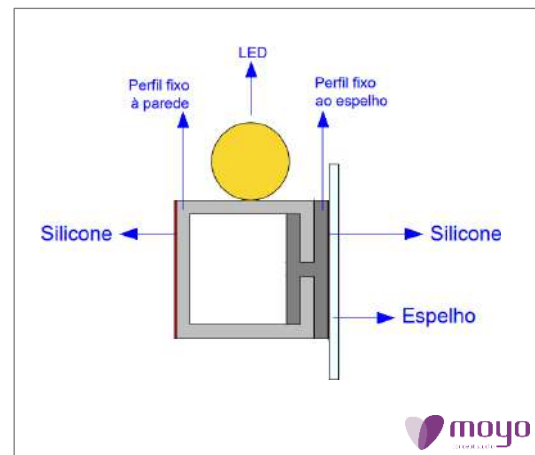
Desenho Técnico da estrutura de fixação Nº1
